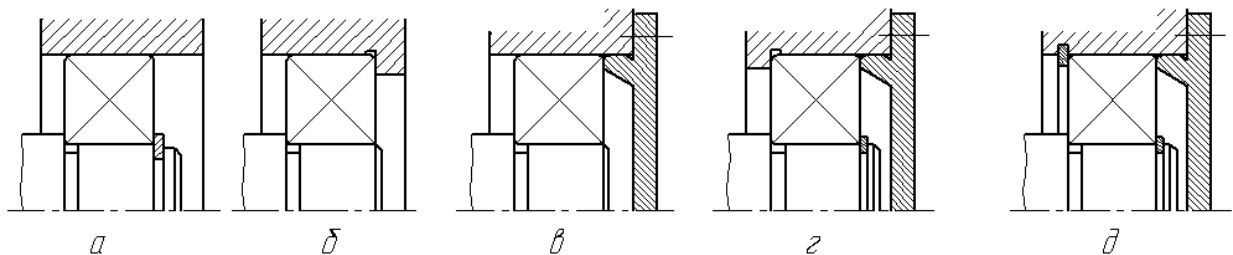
Закріплення підшипників кочення у корпусі опори
